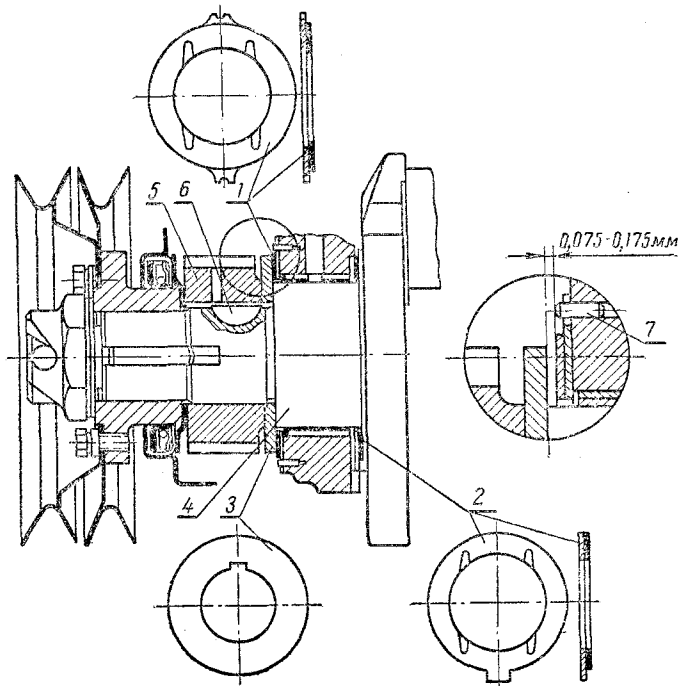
Первый коренной подшипник коленчатого вала двигателей ГАЗ-52-01 и ГАЗ-69:
